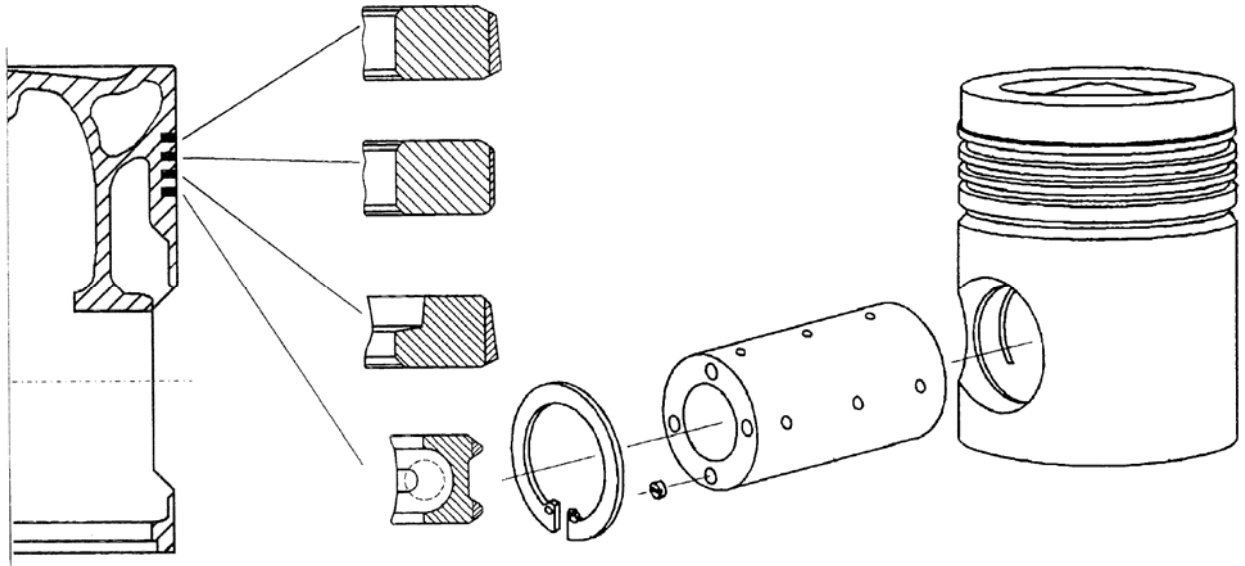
Загальний вигляд та конструкція поршня та поршневих кілець дизеля L28/32
